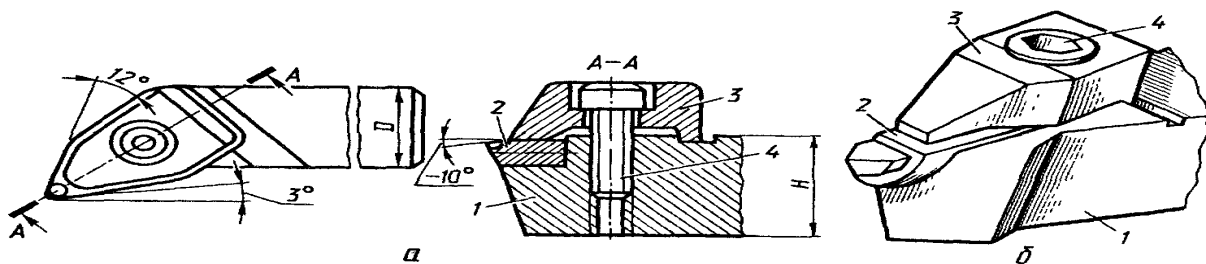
Різець для тонкого точіння по сталі, оснащений композитом: а - креслення; б - загальний вигляд; 1 - державка; 2 - вставка з композитом; 3 - притискна планка, 4 - гвинт
